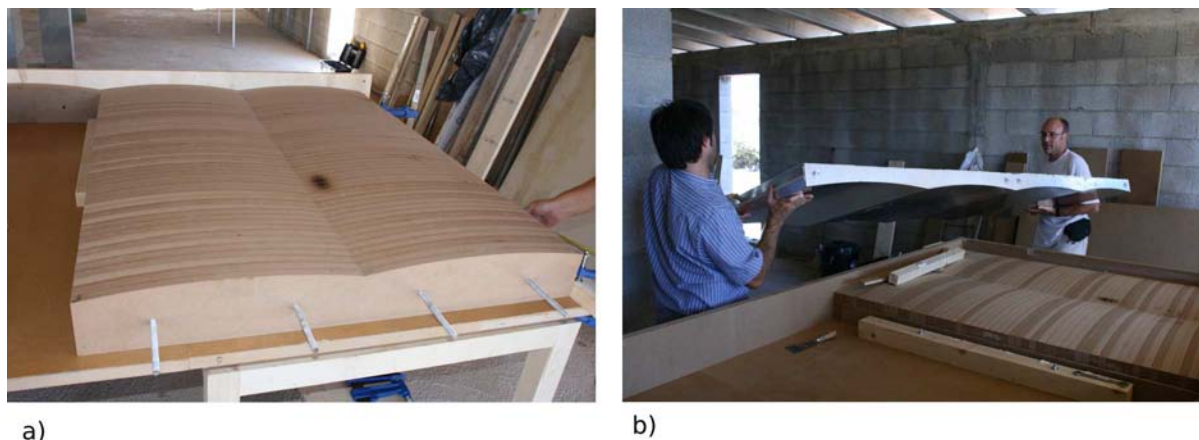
a) Molde para la fabricación del panel reflector. b) Imagen de un proceso de desmoldado
